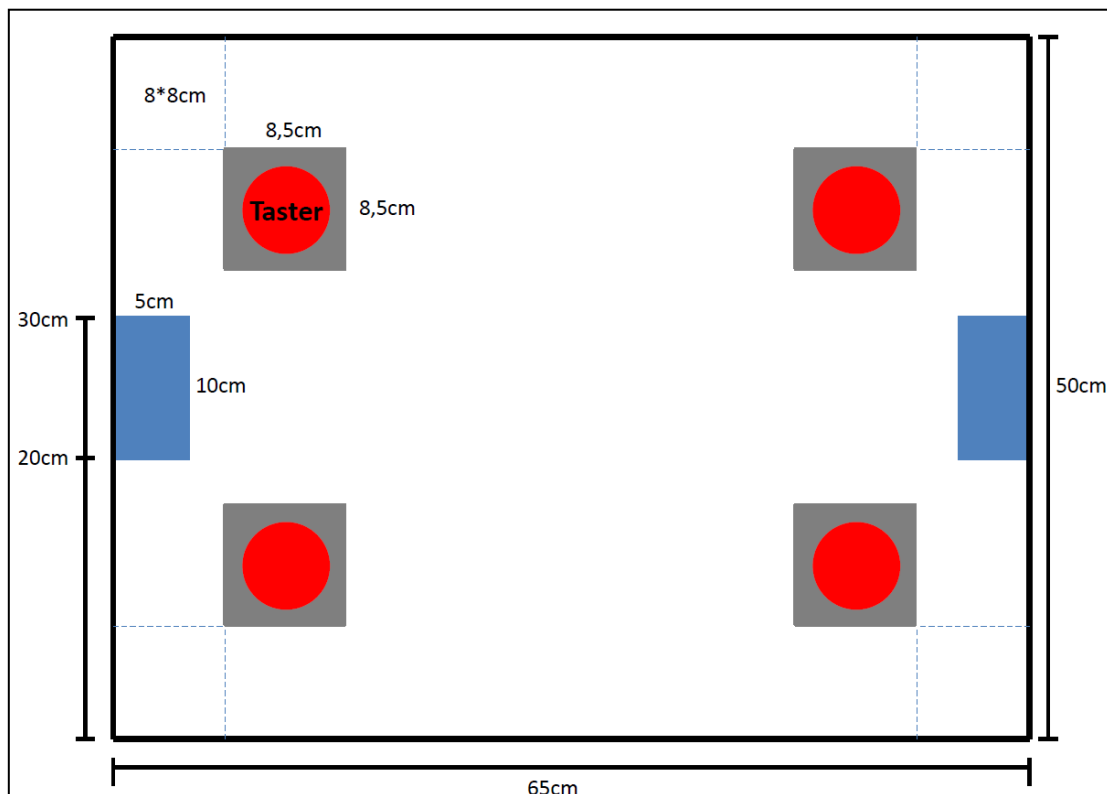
Draufsicht auf Stehpult-Arbeitsplatte mit Tastern und Markierungsflächen für die Hände.
